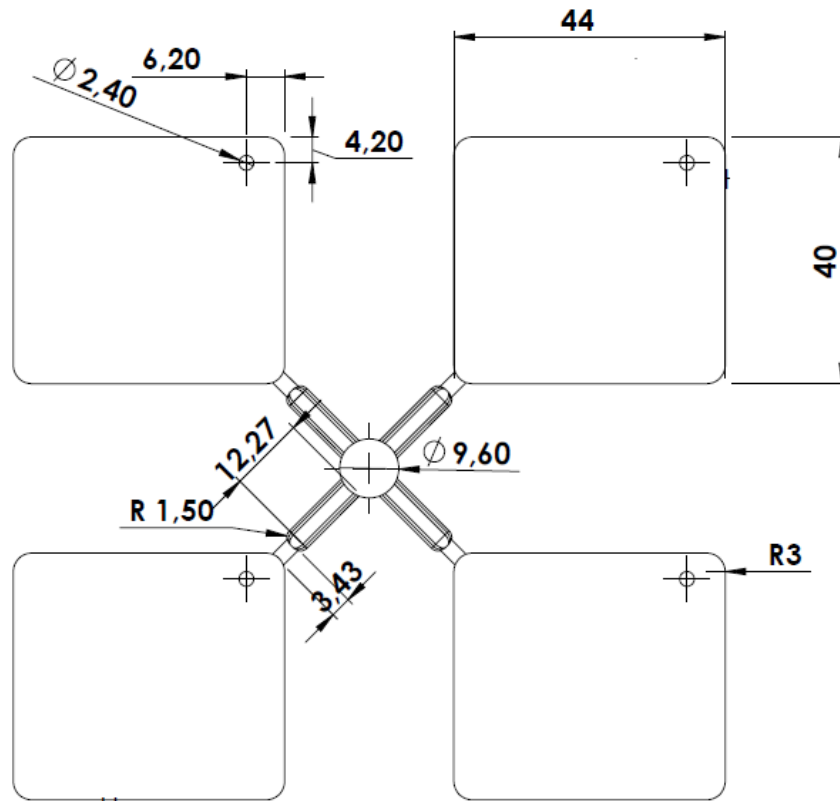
Plano bidimensional del sistema de alimentación del molde de inyección. Fuente: Autor
